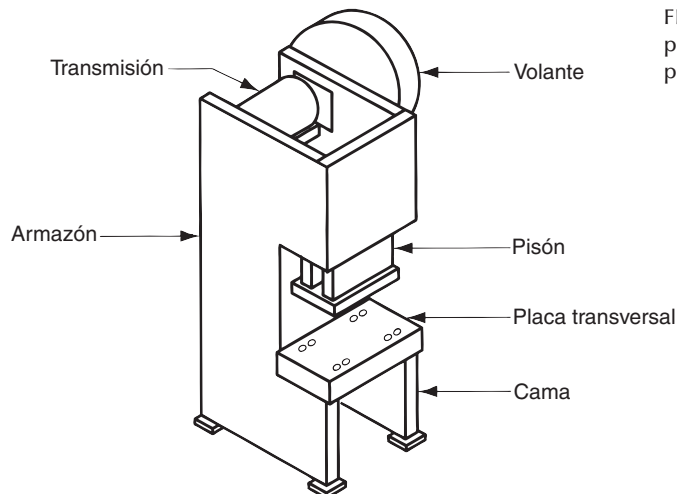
Componentes de una prensa troqueladora típica accionada por transmisión mecánica.
